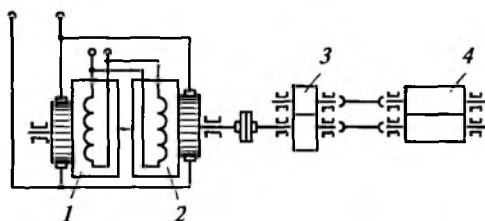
Главный привод прокатного стана с двухъякорным двигателем:
